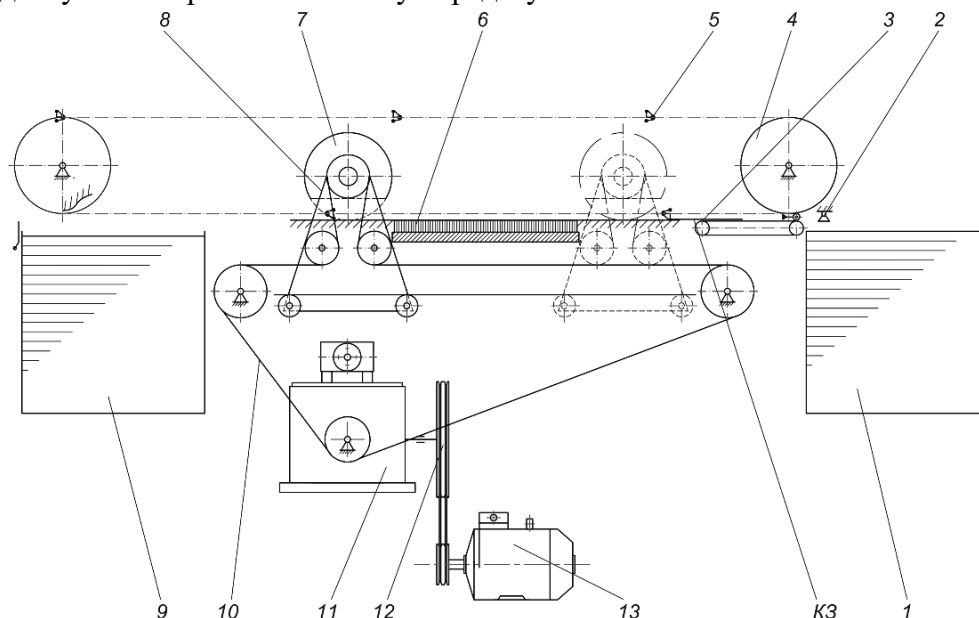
Кінематична схема плоскоциліндрового штанцювального преса:
